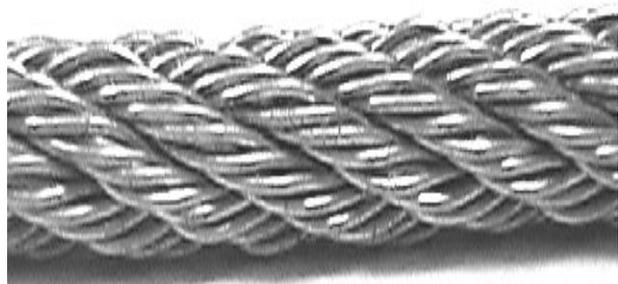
Образец № 1 каната двойной свивки диаметром 3,4 мм изготовленный с неравномерным натяжением
